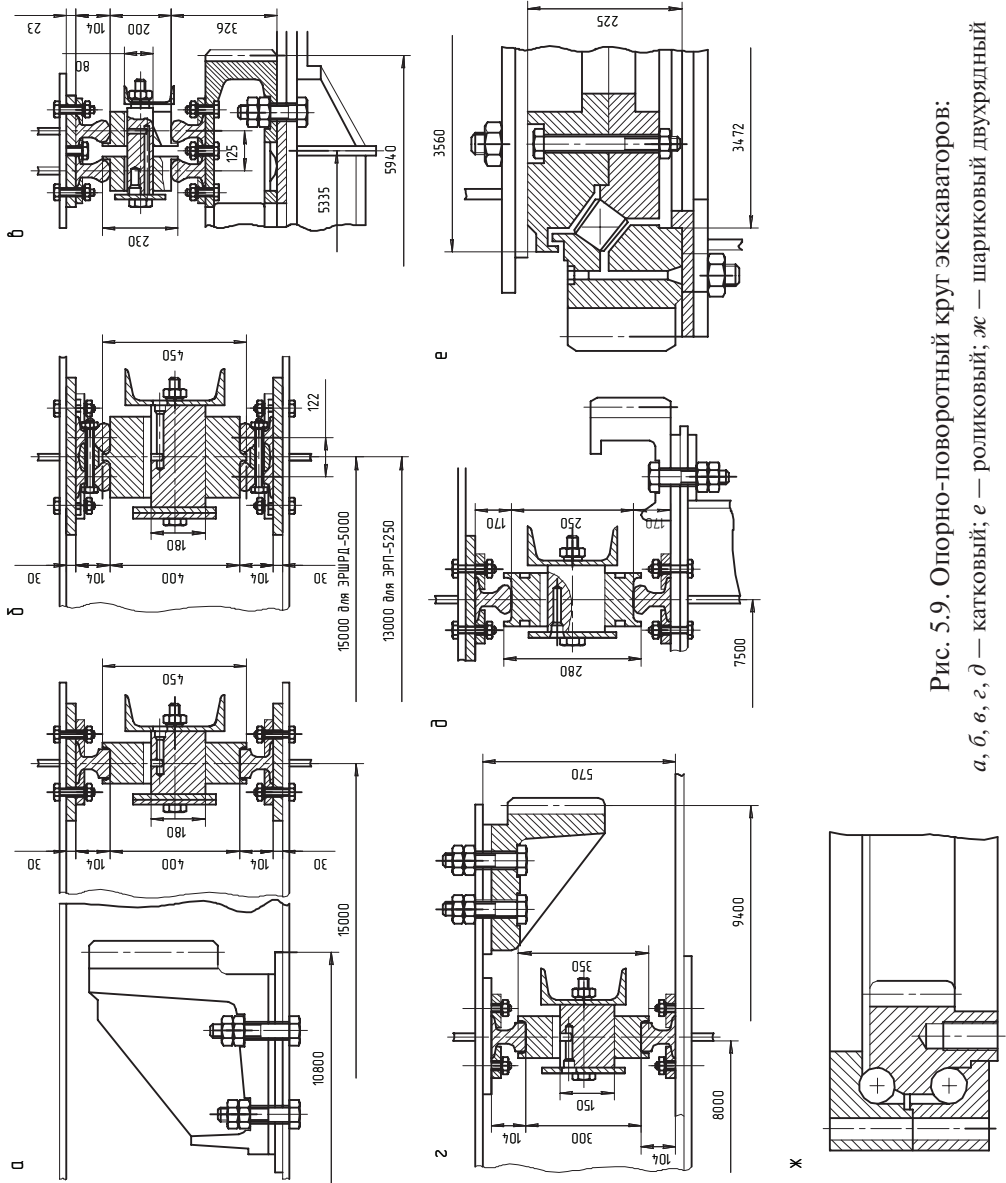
Опорно-поворотный круг экскаваторов:
